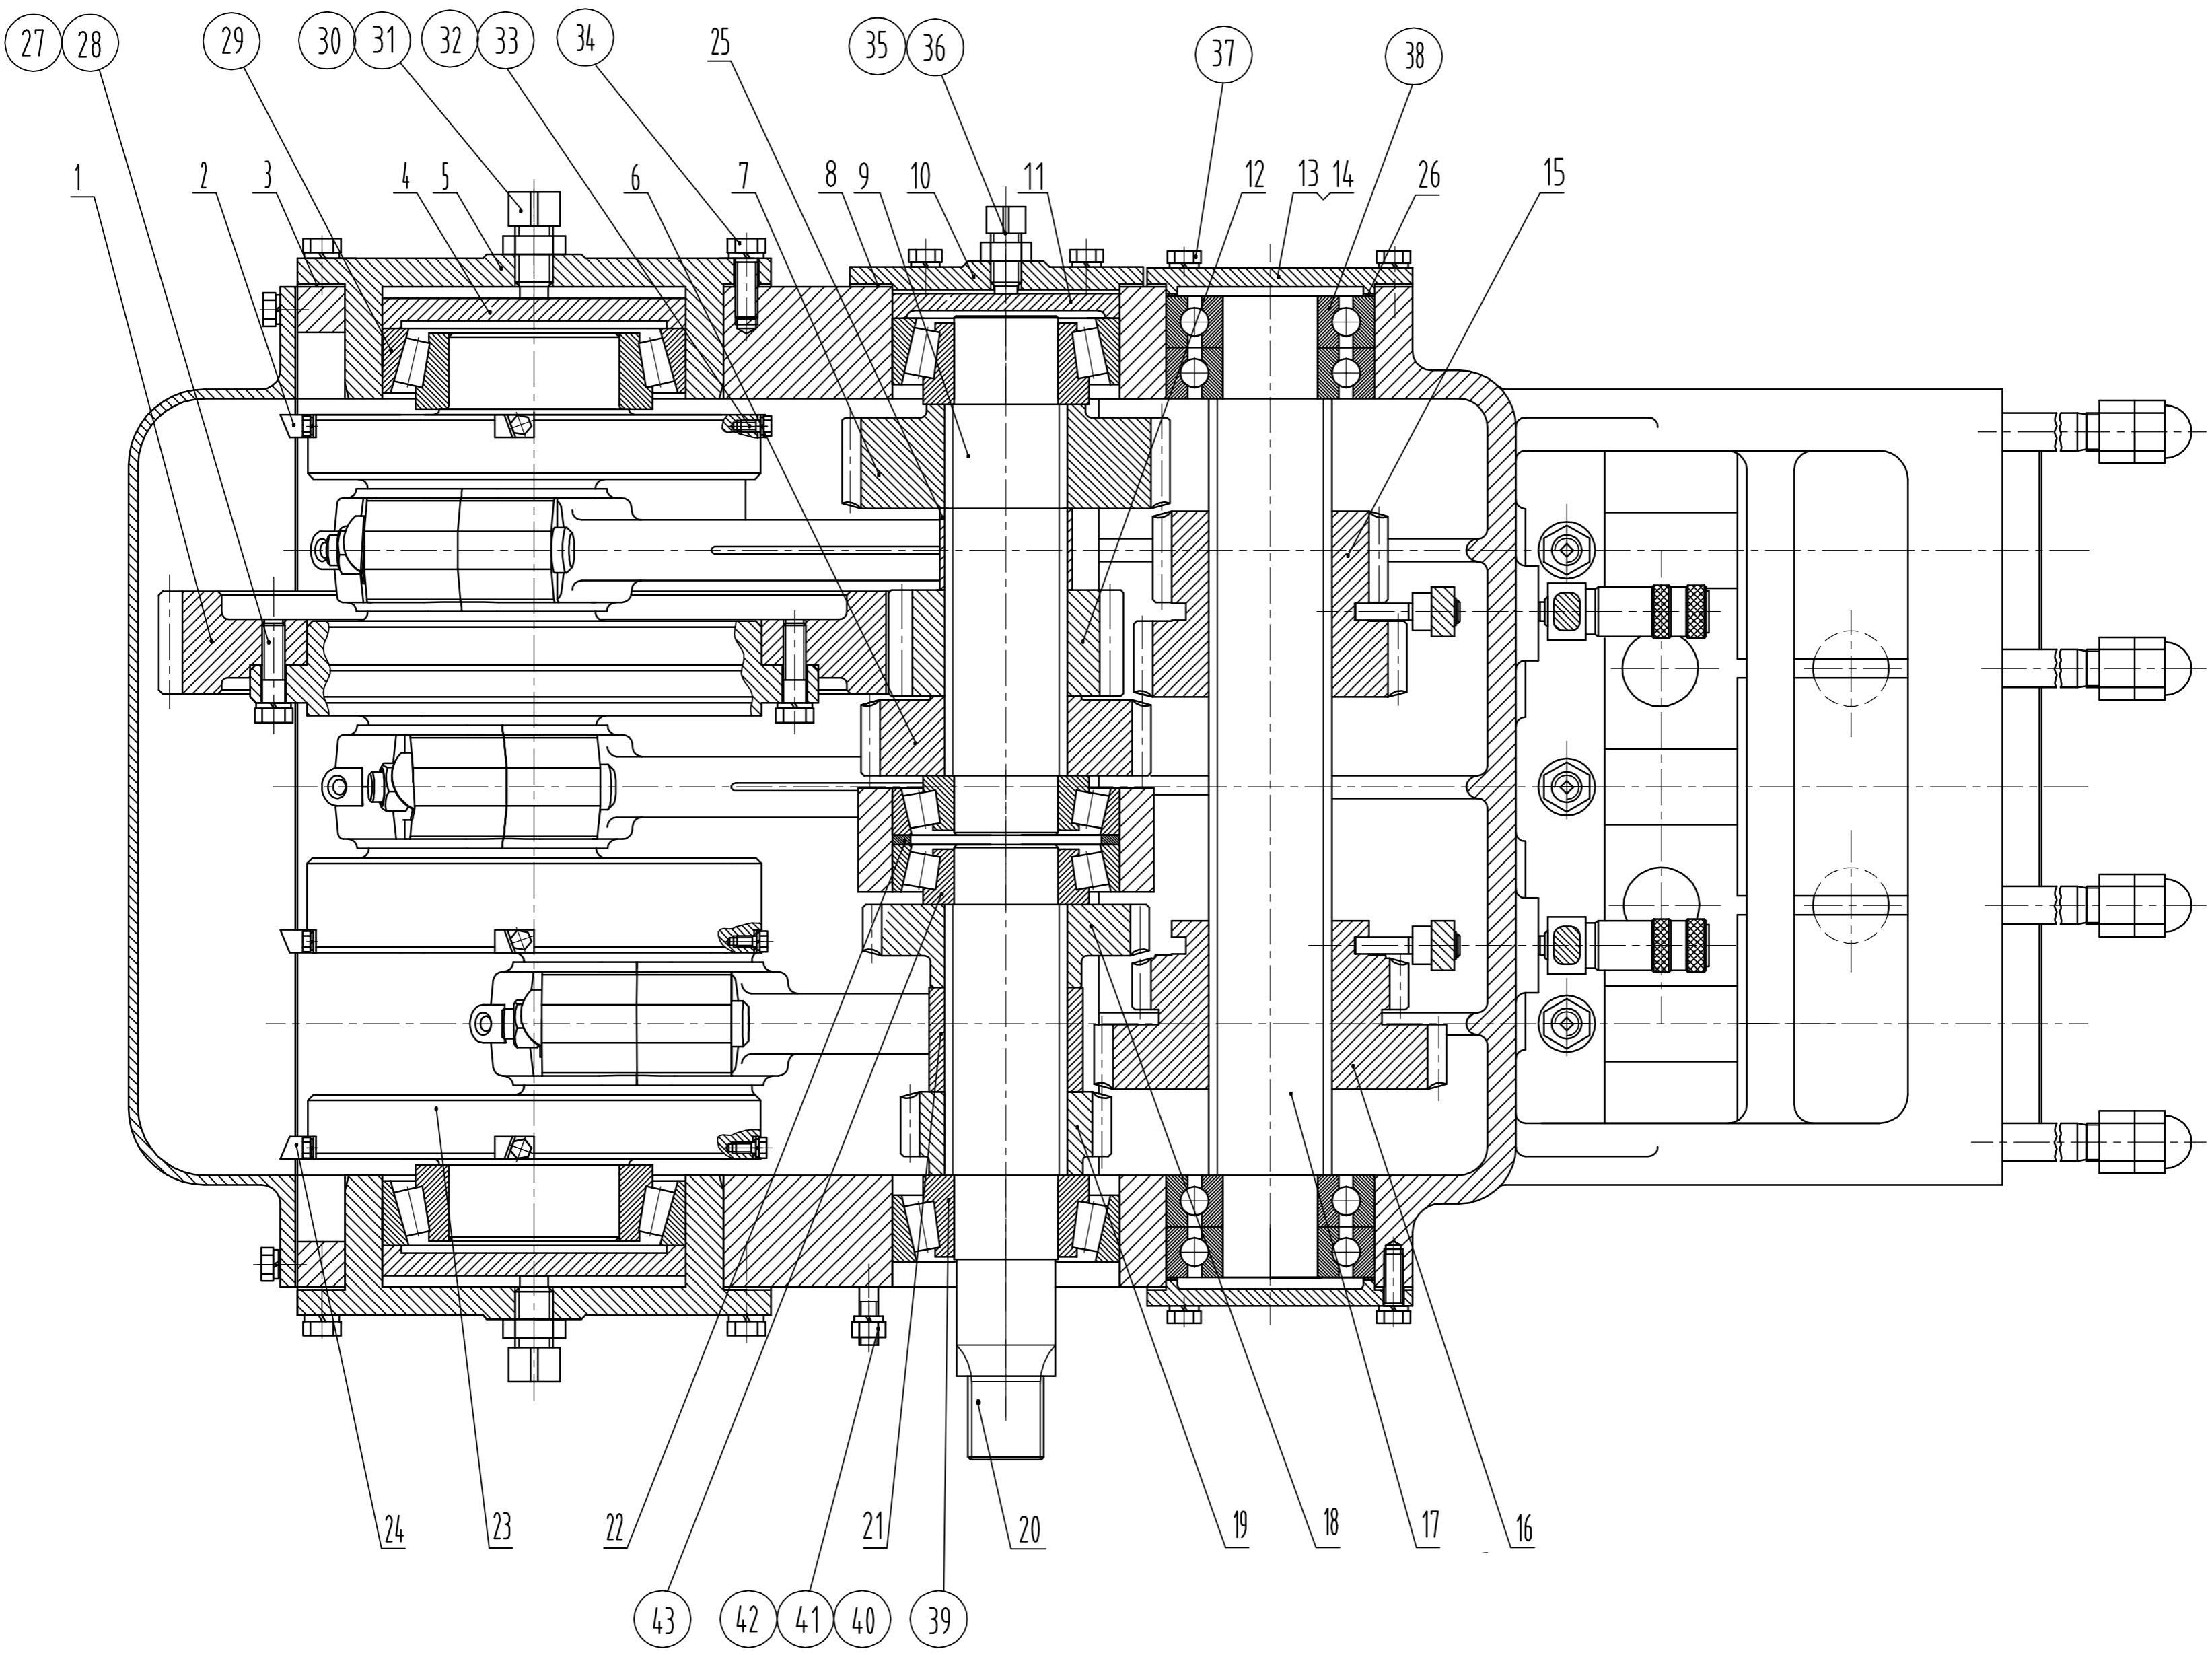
Схема установки корпуса насоса BW600-02M-00
